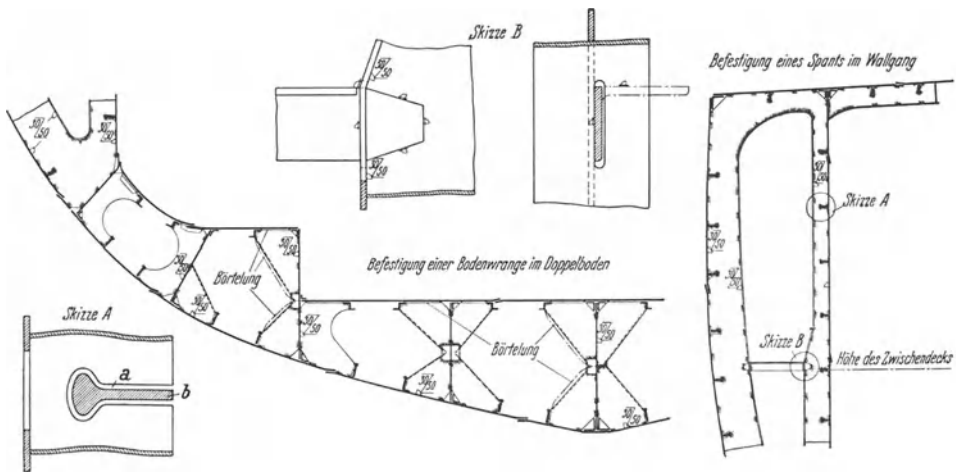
Bodenwrange und Spant eines Torpedoboots, geschweißt.
